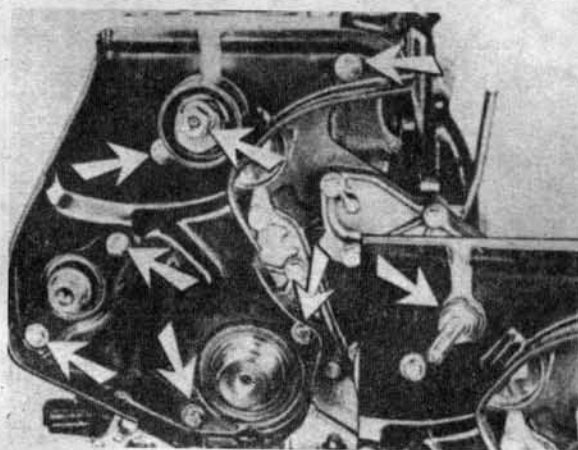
Снятие валика-натяжителя зубчатого ремня привода механизма газораспределения
